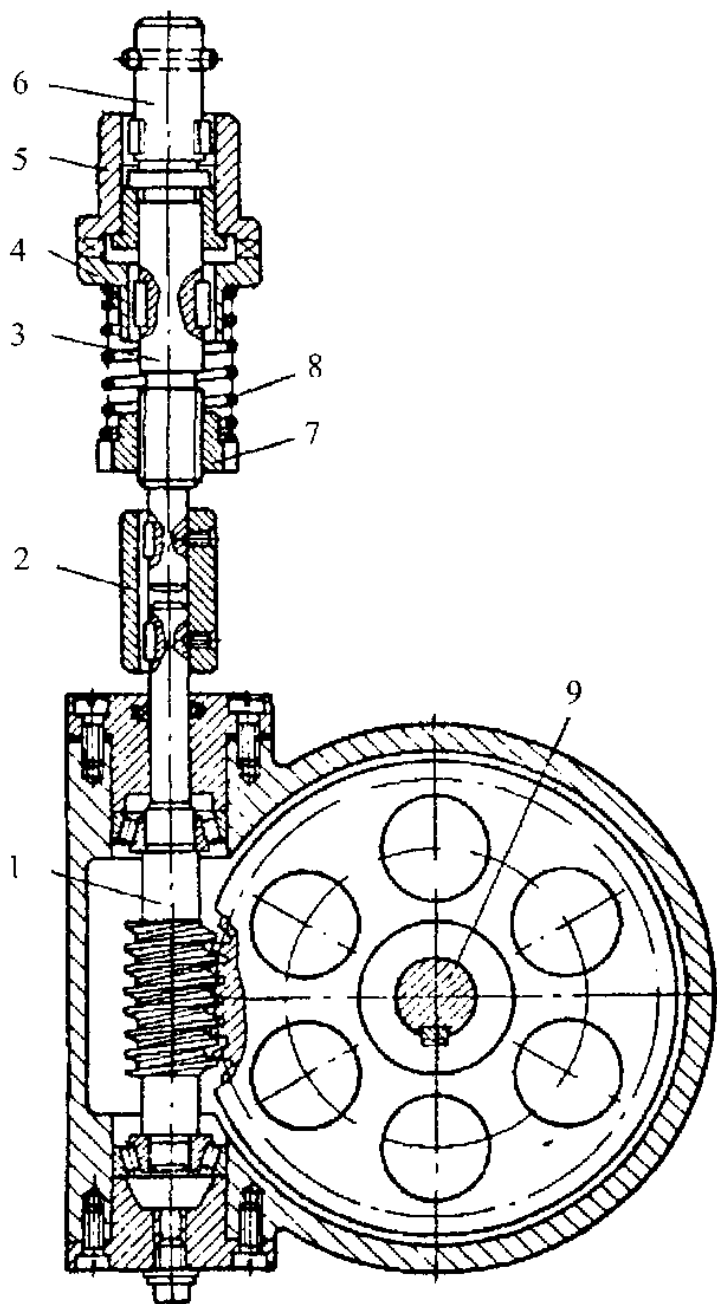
Черв'ячний привод для механізації повороту пристрою
